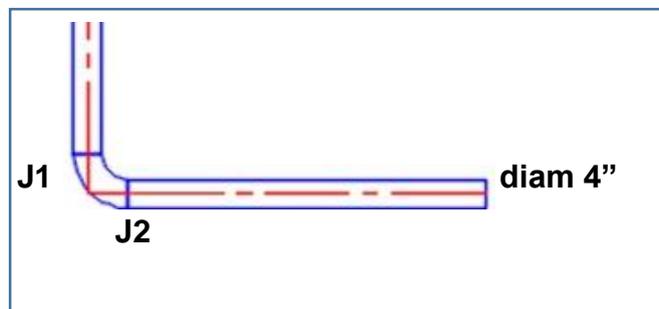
Juntas de tuberías a soldar. Fuente: elab propia
